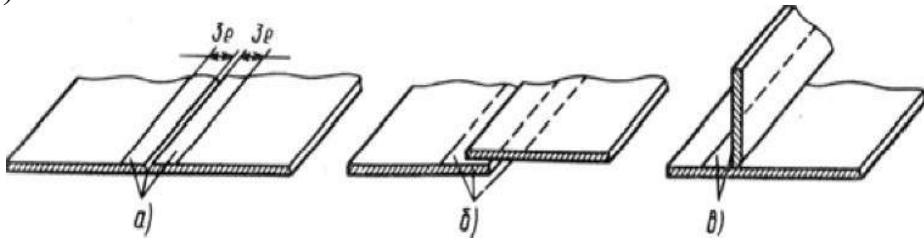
Подготовка кромок к пайке латунным припоем: а - участки, зачищенные до металла; б и в - зачистка до чистого металла
